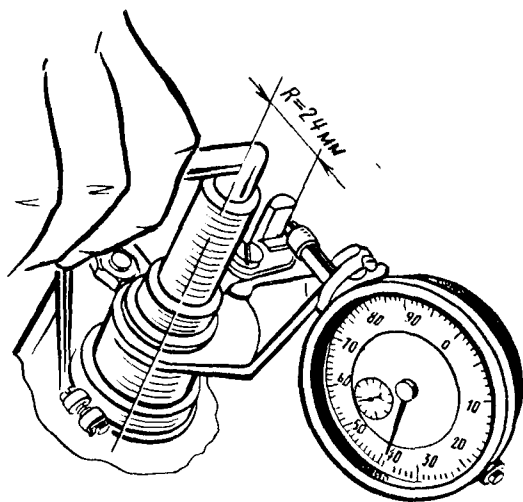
Проверка бокового зазора в зацеплении шестерен привода датчика-распределителя
